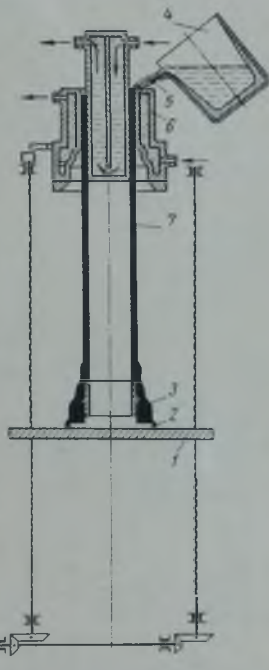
Схема отливки труб с растробой полунепрерывным способом
